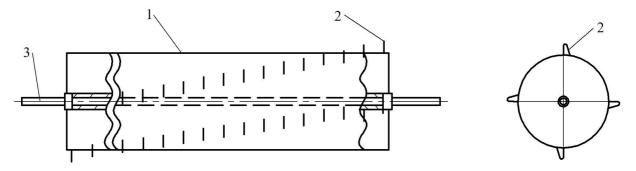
Фреза: 1 - барабан; 2 - нож; 3 - вал
